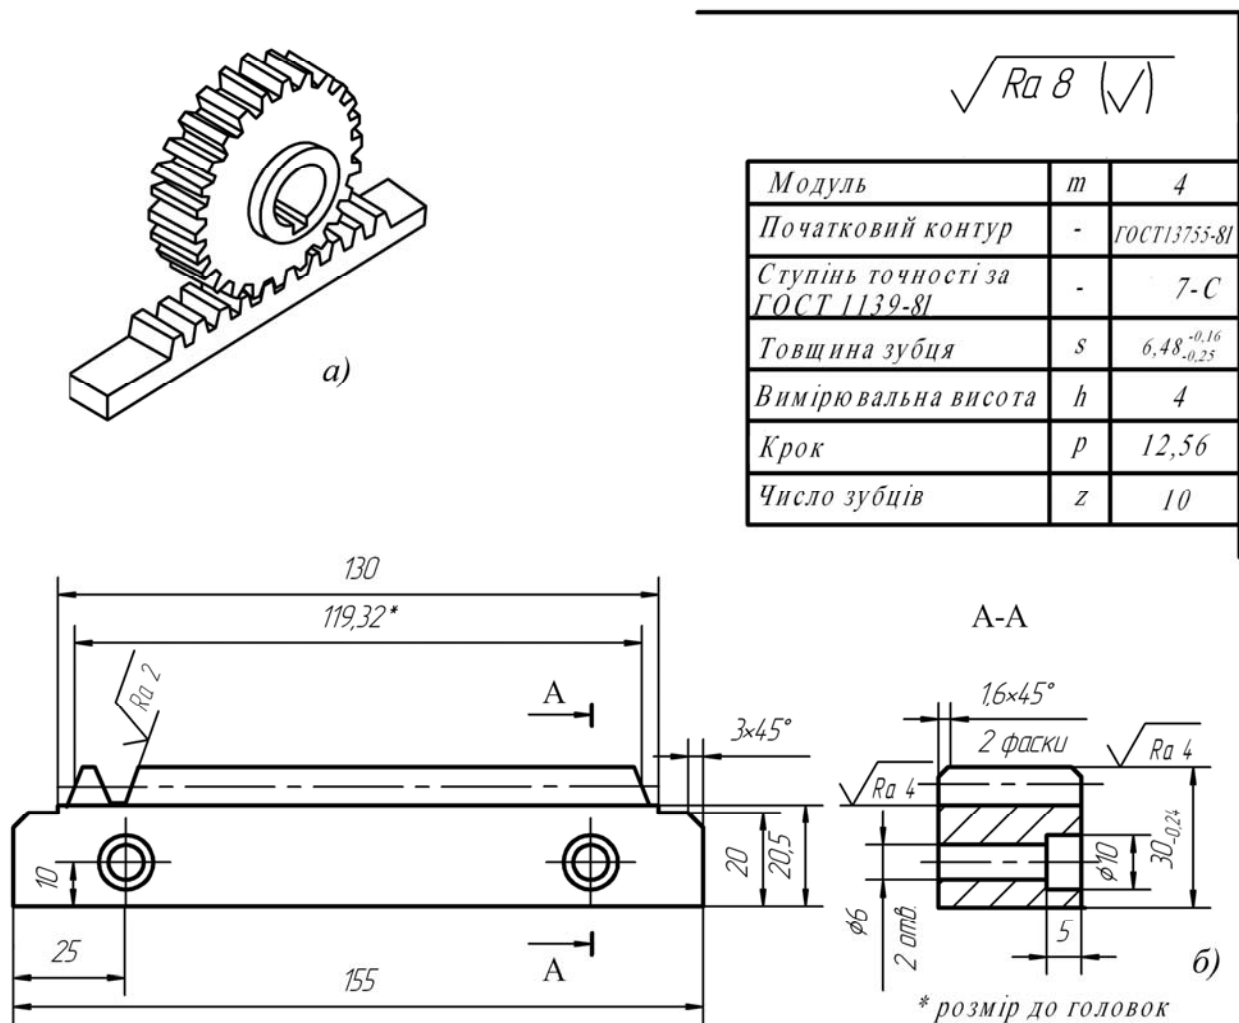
Зображення рейкової передачі: *a* – наочний вигляд; *б* – приклад робочого кресленника зубчастої рейки
